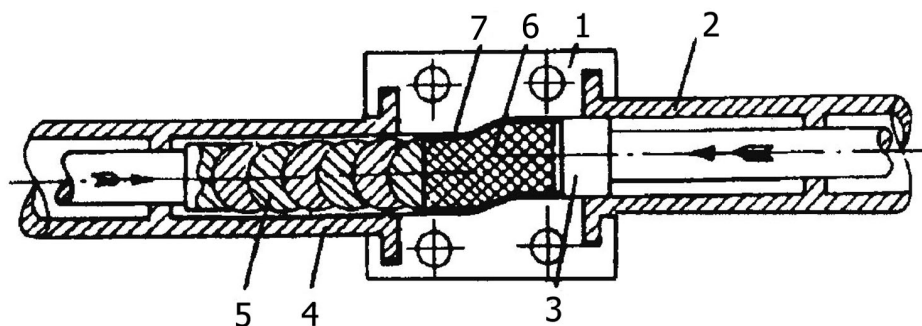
Схема устройства для формообразования ступенчатого патрубка:
